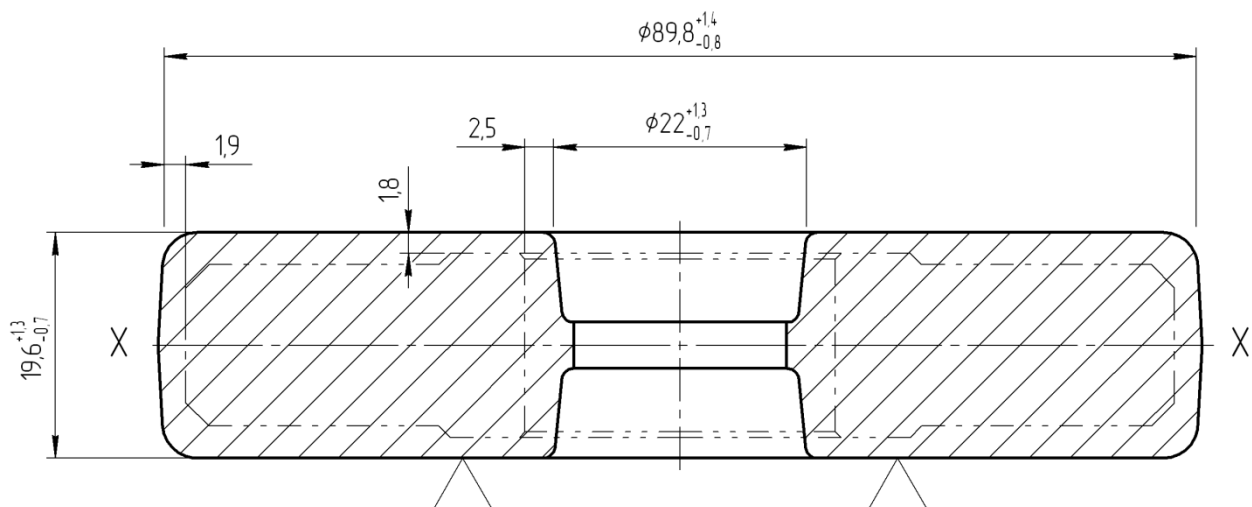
Заготовка корпуса дисковой фрезы
